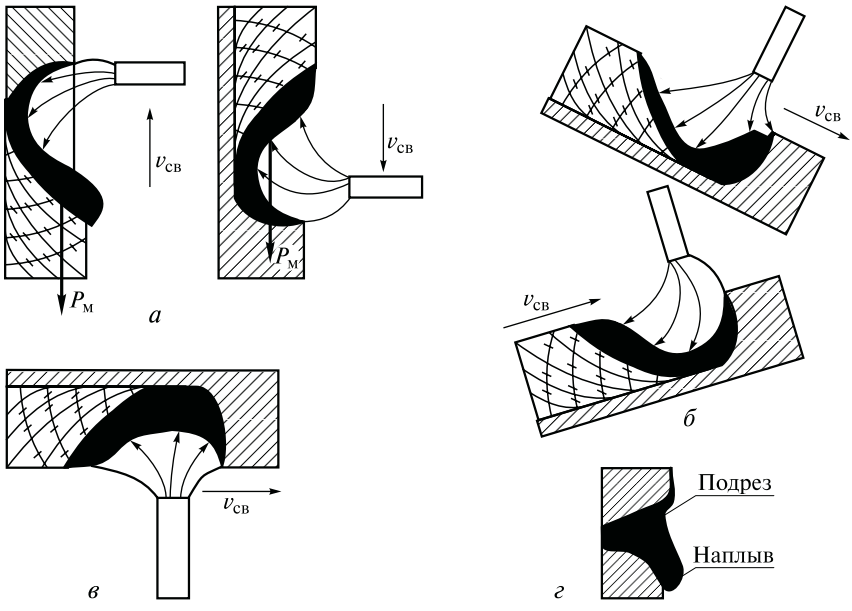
Формирование сварочной ванны в разных положениях: *а* — вертикальном; *б* — наклонном; *в* — потолочном; *г* — горизонтальном; v_{CB} — скорость сварки; P_M — давление жидкого металла
